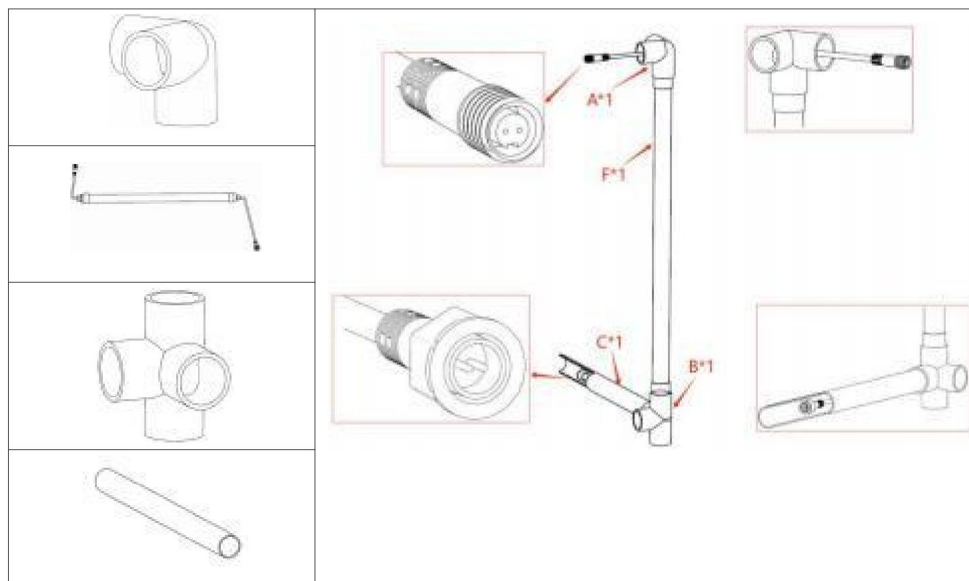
Assemblez un tube horizontal de 355 mm, un tube à 4 passages, un tube à 3 passages et une lampe ensemble comme indiqué sur la figure (notez que le fil de la lampe se trouve dans le trou des 3 barillets et de la sortie à 4 passages).
